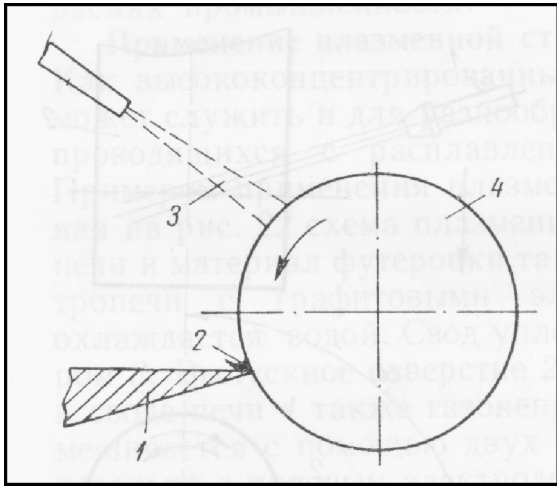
Сполучене точіння (плазмовим струменем та різцем): 1 - різець; 2 - стружка; 3 - плазмовий факел; 4 - заготовка, що обробляється
